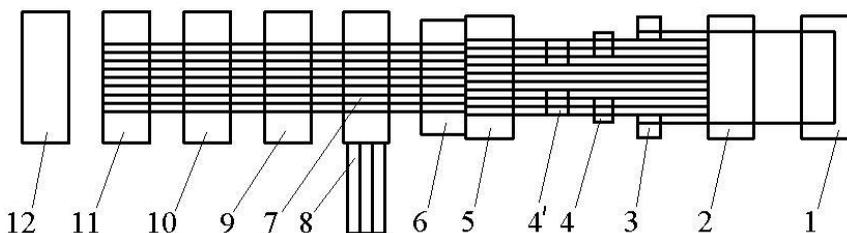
Схема автоматической линии изготовления решетчатого настила.
